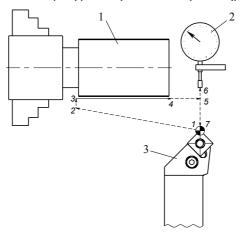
Методика измерения температурного удлинения сборного токарного резца на станке с ЧПУ: 1 — заготовка; 2 — индикатор (1-ИГМ); 3 — сборный токарный резец
